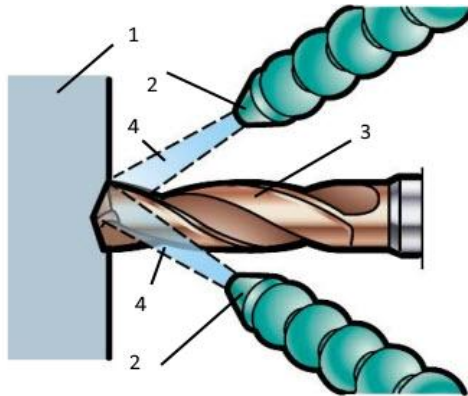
Свердло з зовнішнім підводом МОР: 1 – заготовка; 2- сопло; 3 – свердло; 4 – МОР.
